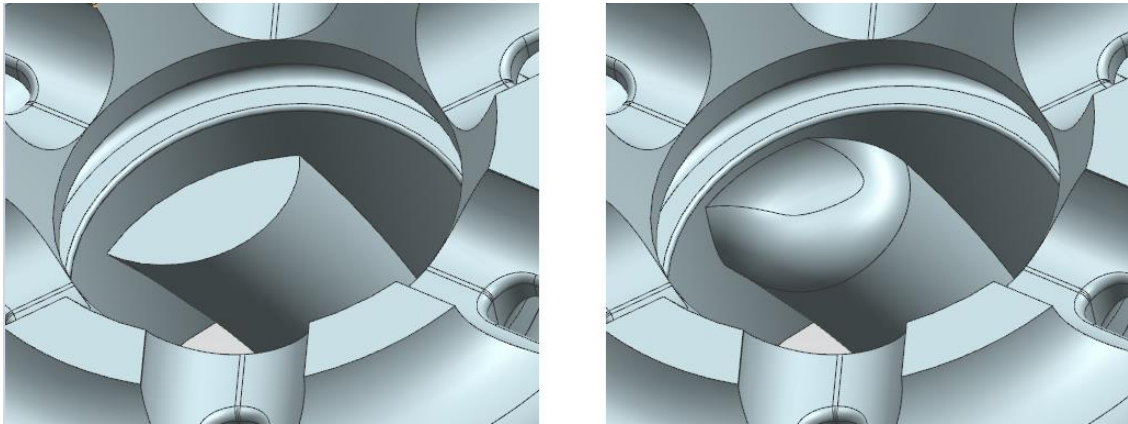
a) Detailní pohled na výstup / b) Zobrazení chlazení hřbetu frézy
